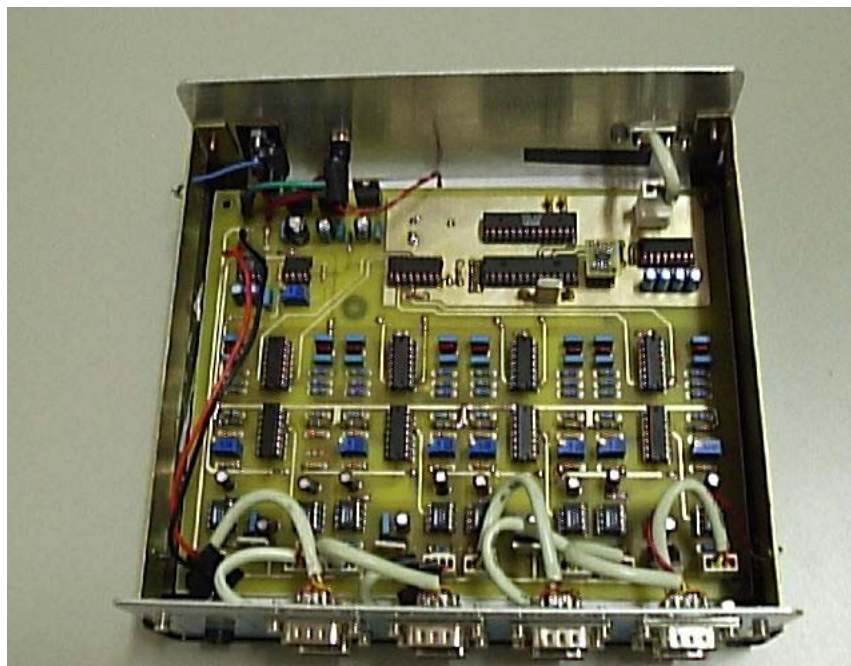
Foto da disposição dos componentes no módulo condicionador de sinais.
